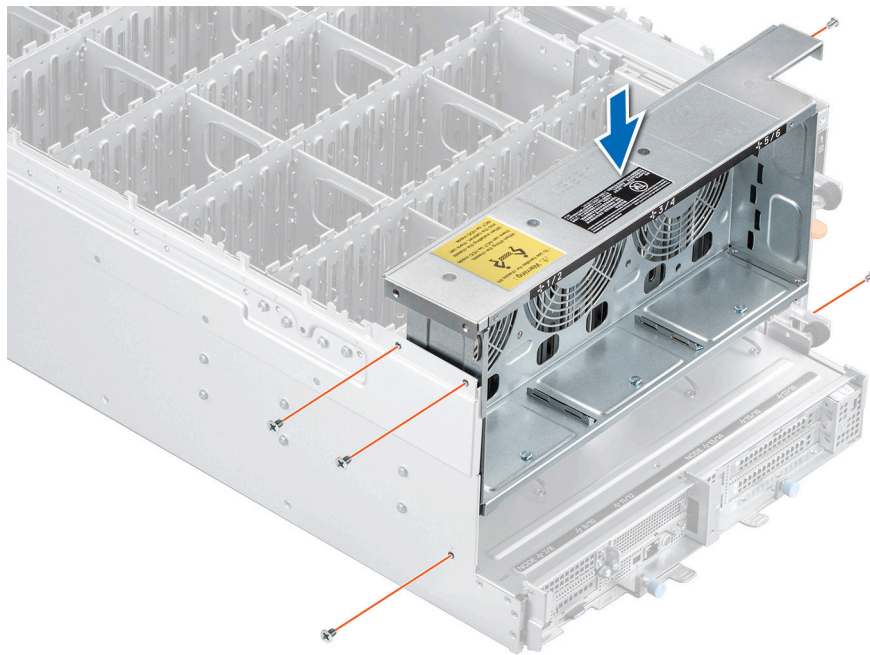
Installation d'un bâti de ventilateur de refroidissement
